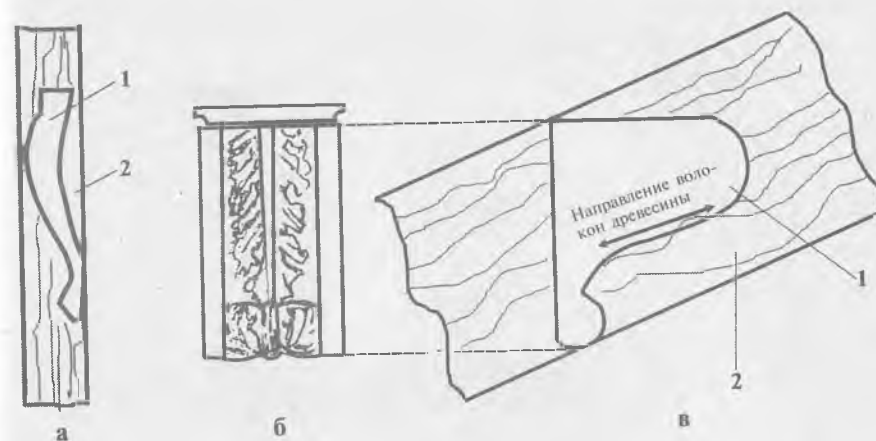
Лекала для разметки профилей криволинейных деталей:
